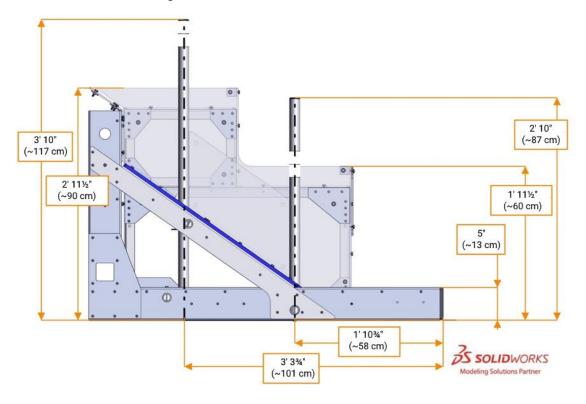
Dimensions du RÉSEAU en vue de dessus
